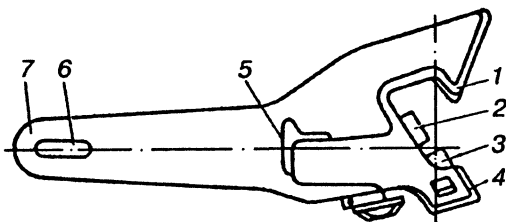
Корпус нежесткой автосцепки в сборе
